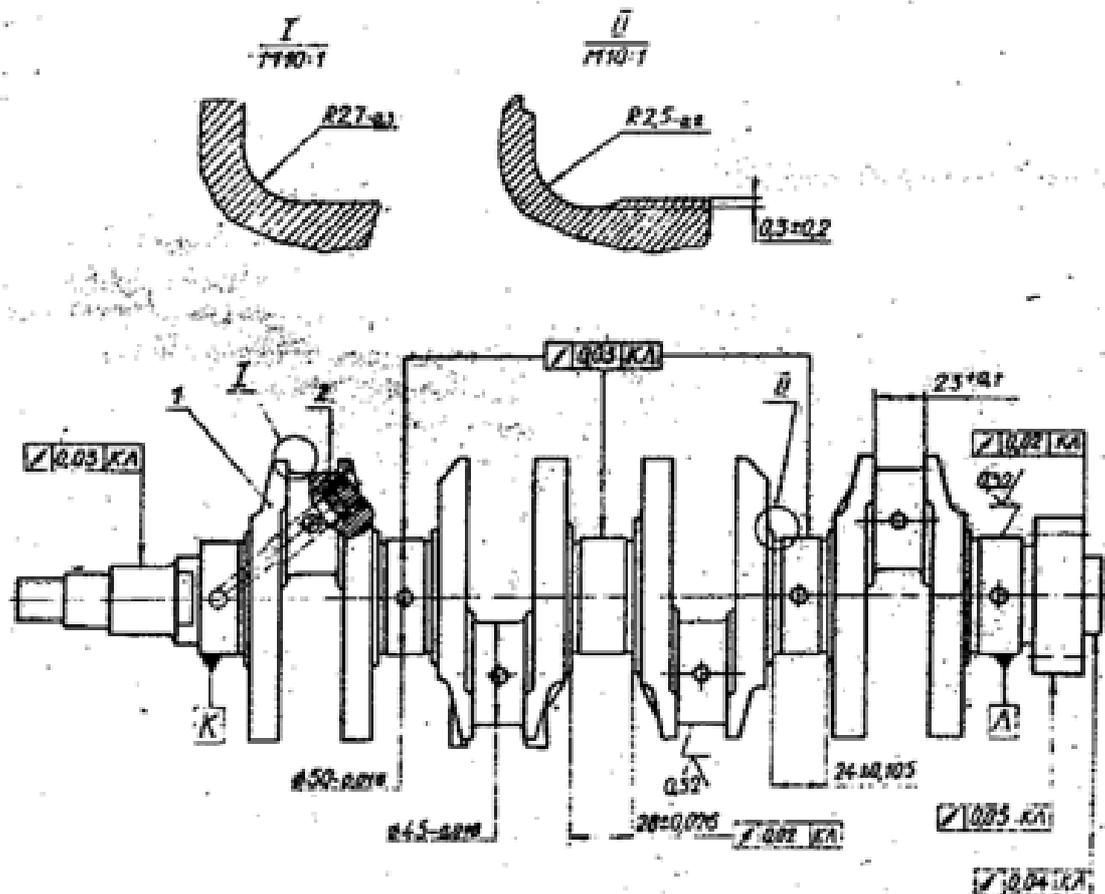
Вал коленчатый в сборе: 1 - вал коленчатый; 2 - пробка
